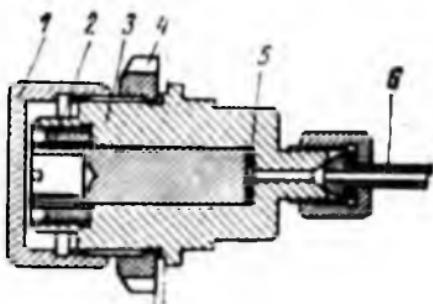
Основание приспособления для регулировки бустерного устройства золотника распределителя:
